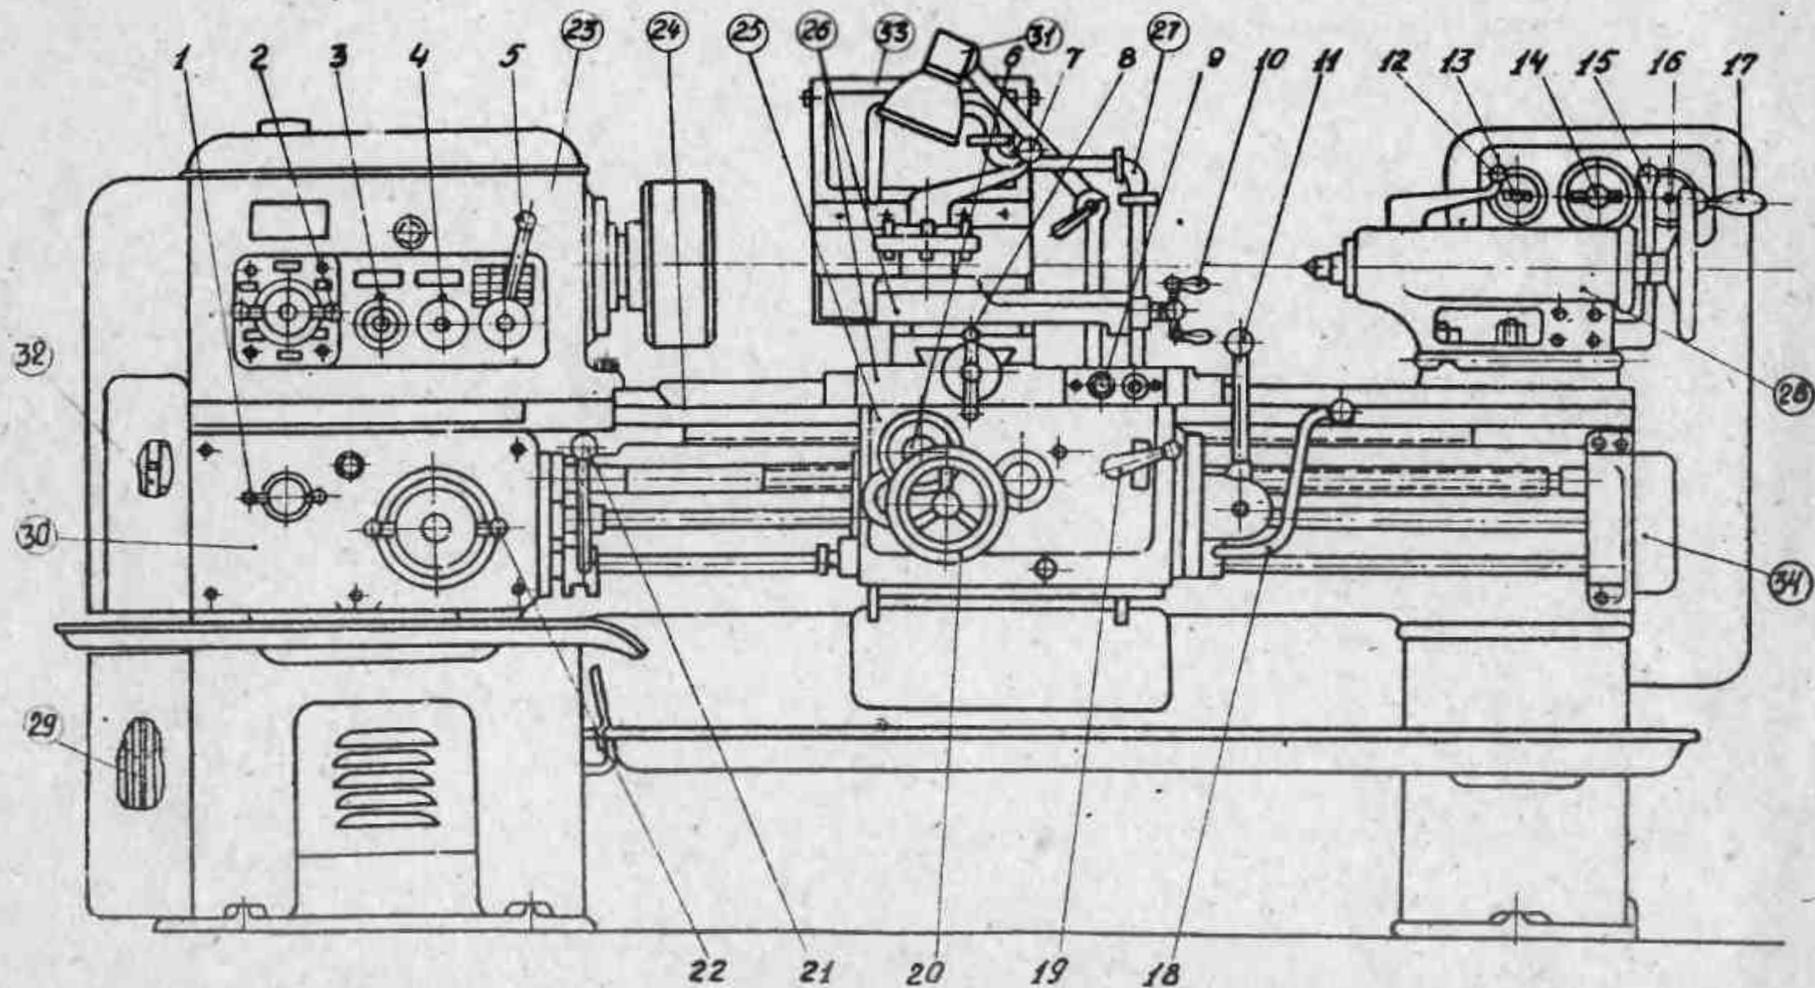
Токарно-винторезный станок 1К62, 1К625
